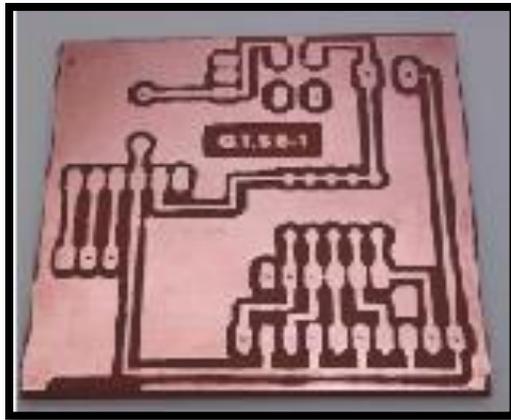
Placa impresa en baquelita de cobre del diseño del segundo circuito
